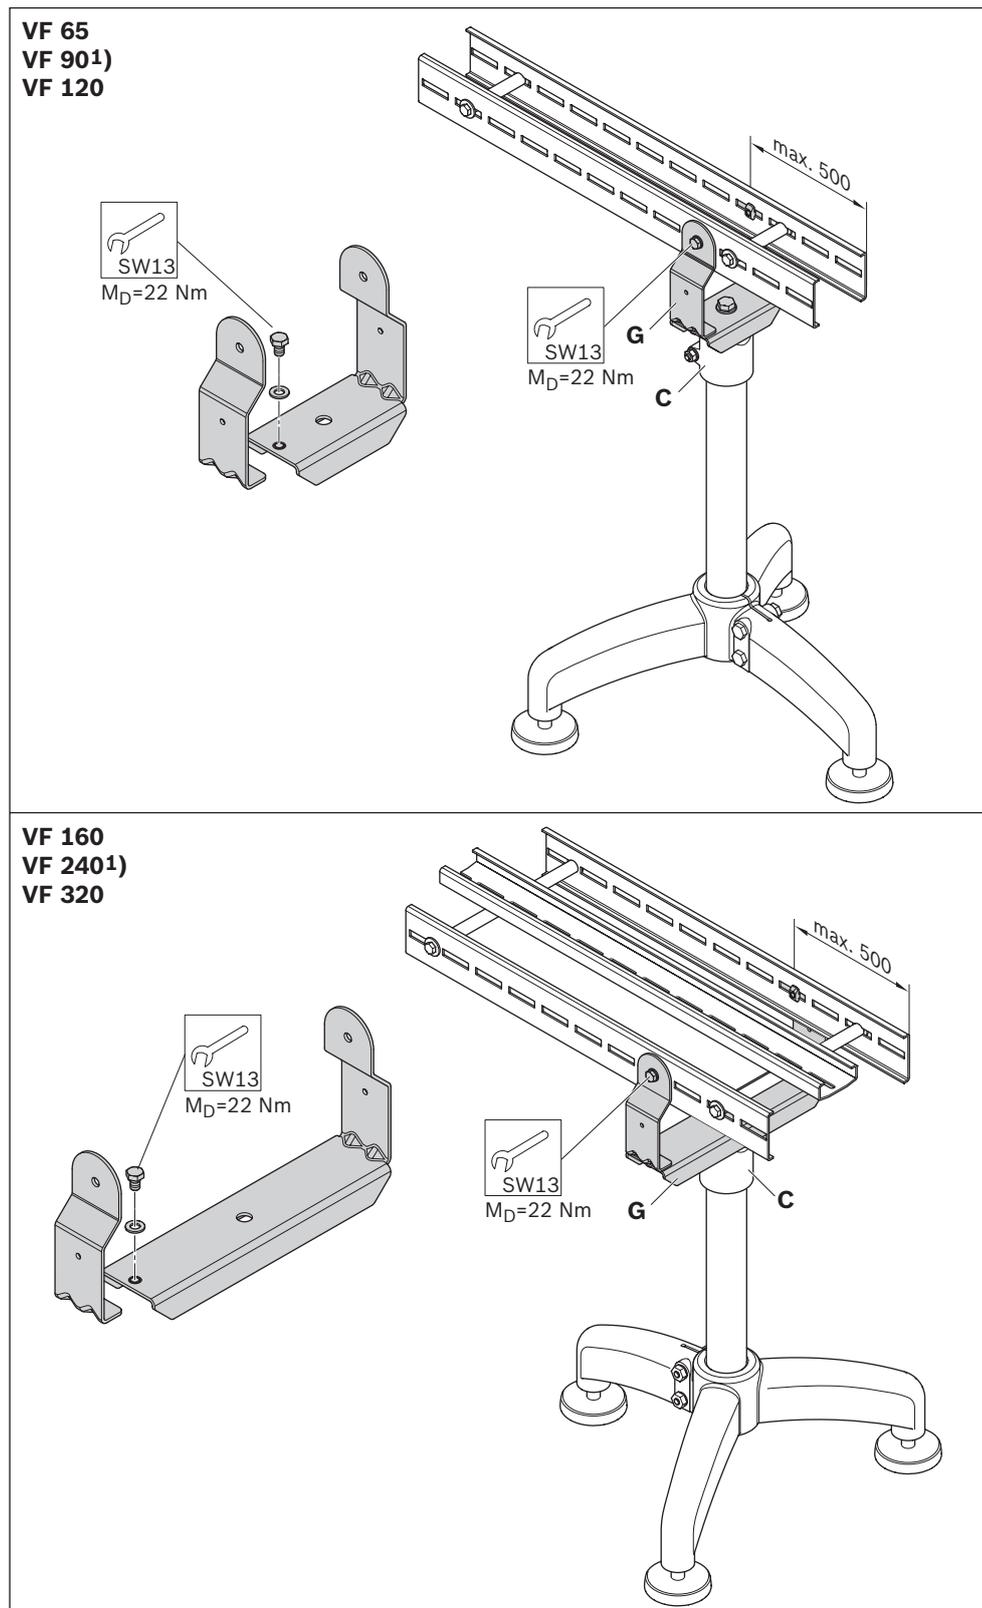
System STS, Strecke auf Streckenstützen montieren
